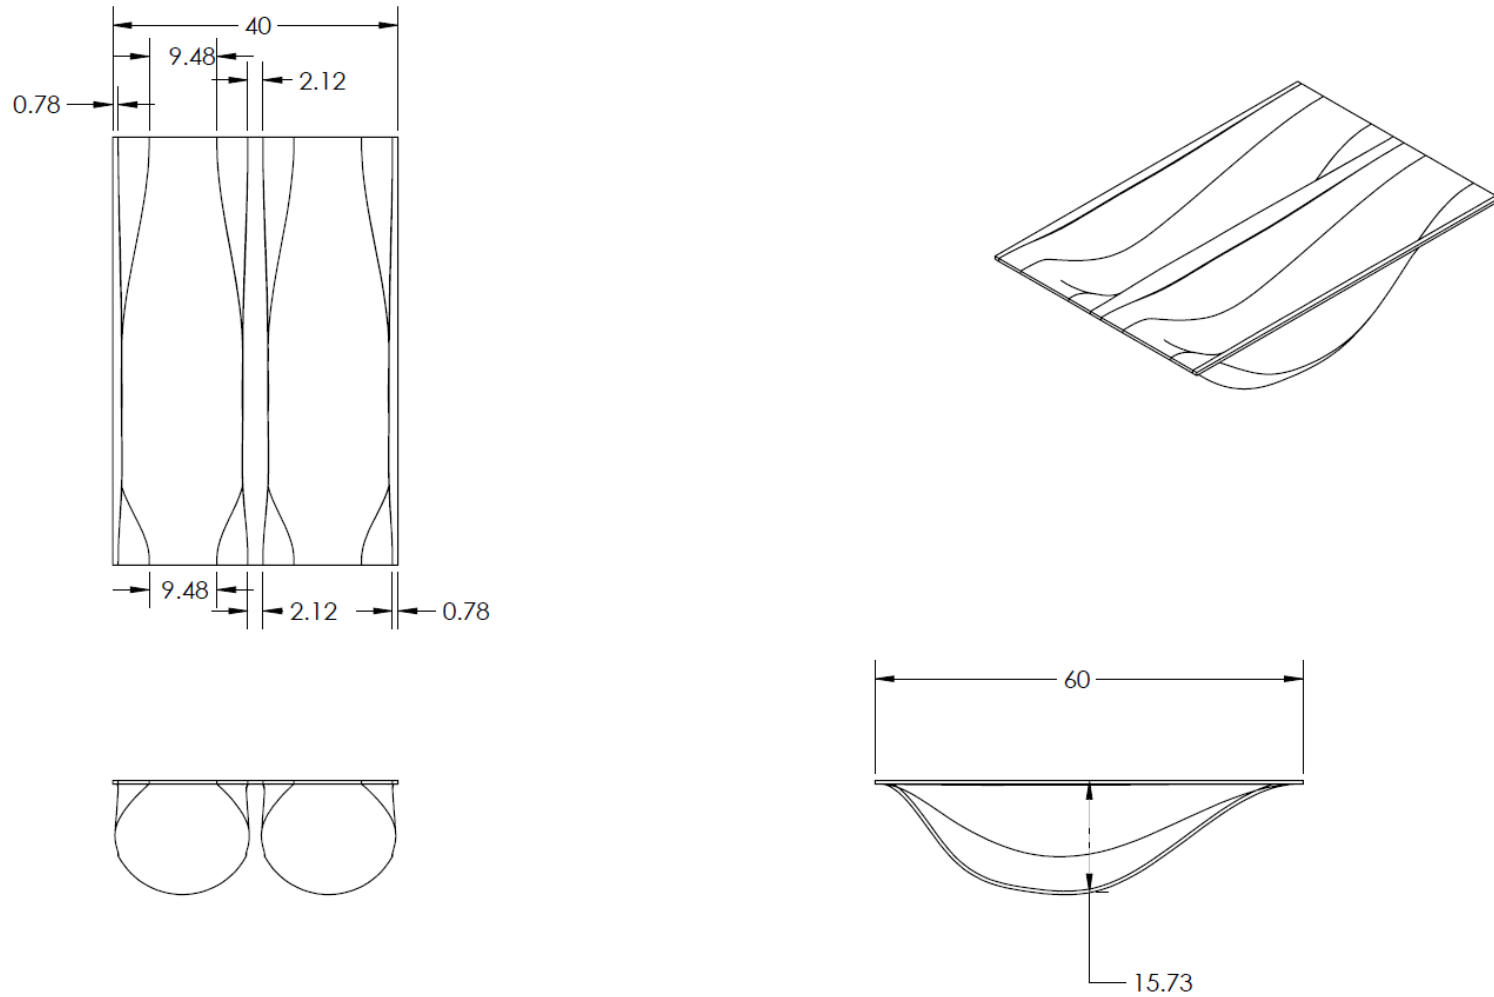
Explosionado 5, Tolva de sachets (Fuente propia)
